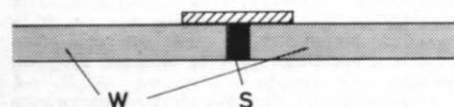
Beim Zusammenkleben der Wandteile W ein gerades Unterlegstück (schraffiert) mit ankleben, den Sägepalt S mit Stabilis ausfüllen und planschleifen!
